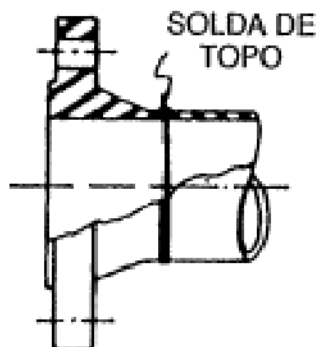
Solda de topo em ligação flangeada entre tubulações.
